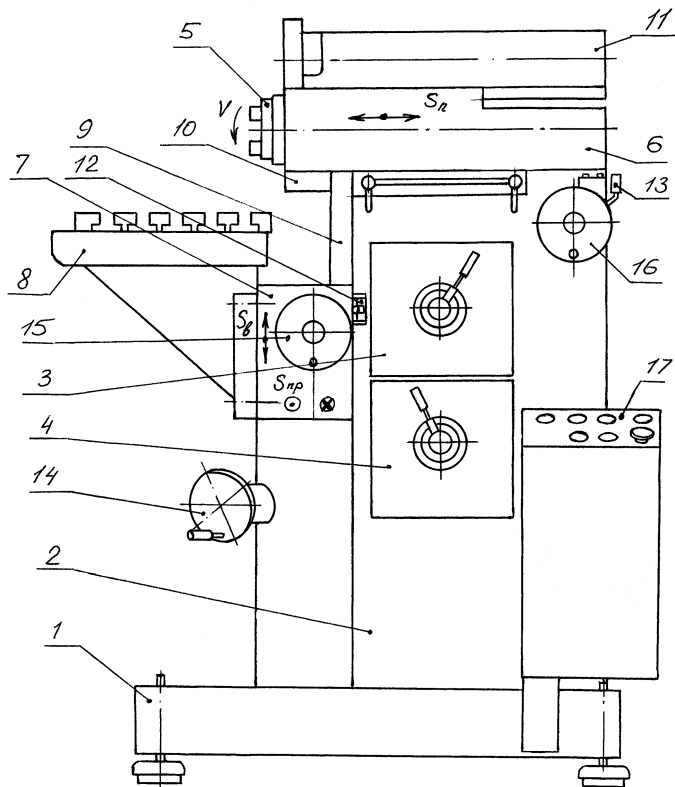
Общий вид горизонтально-фрезерного станка
